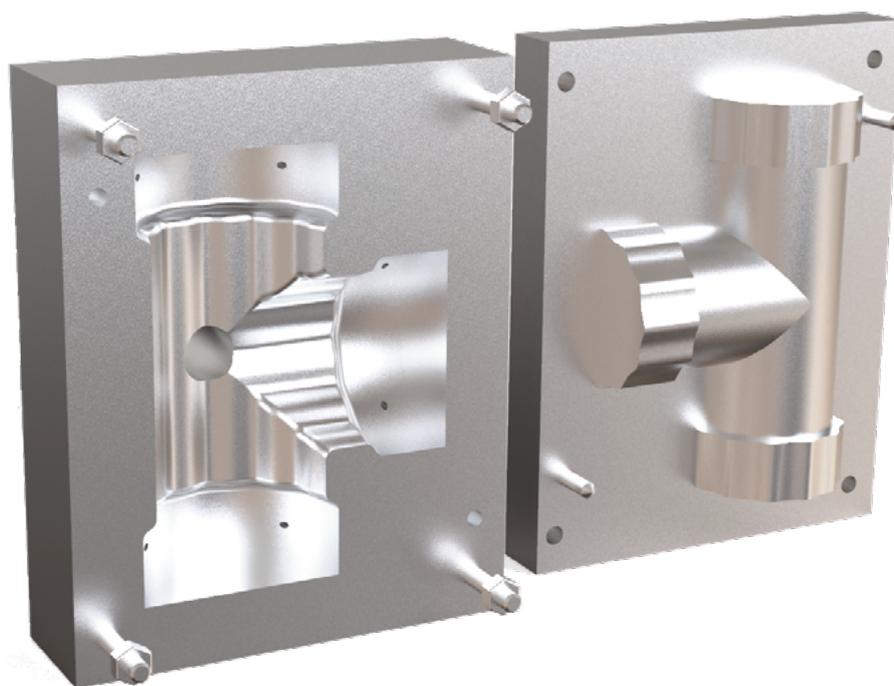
Modelação 3D molde Tê. Realizado pela autora
